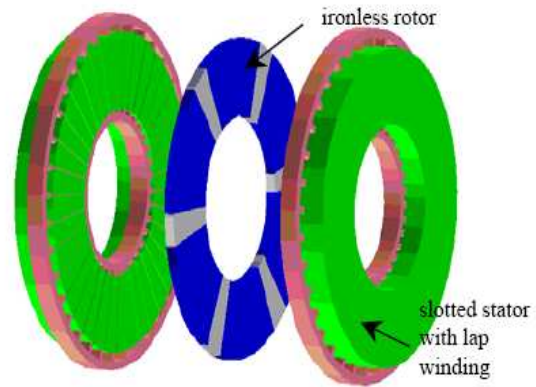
Machine à flux axial à stator externe et bobinage réparti encoché
